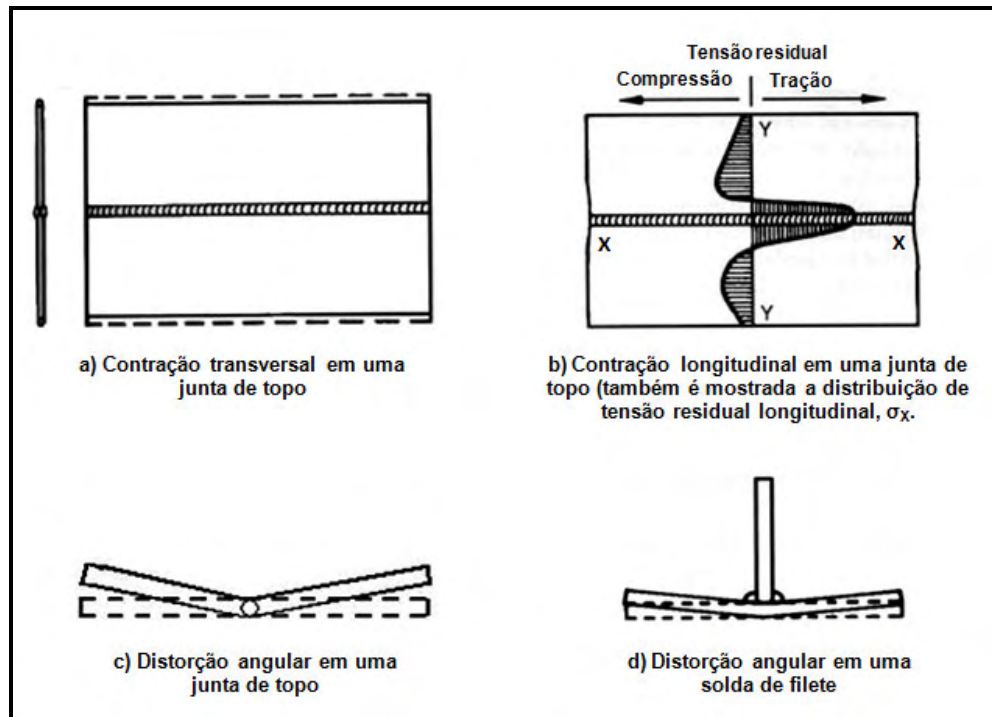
Variações dimensionais fundamentais que ocorrem em soldagem (Adaptado de AWS, 2001).
